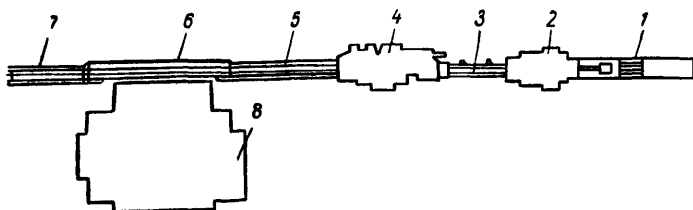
Схема полуавтоматической линии ПЛБ для обработки брусковых деталей.
